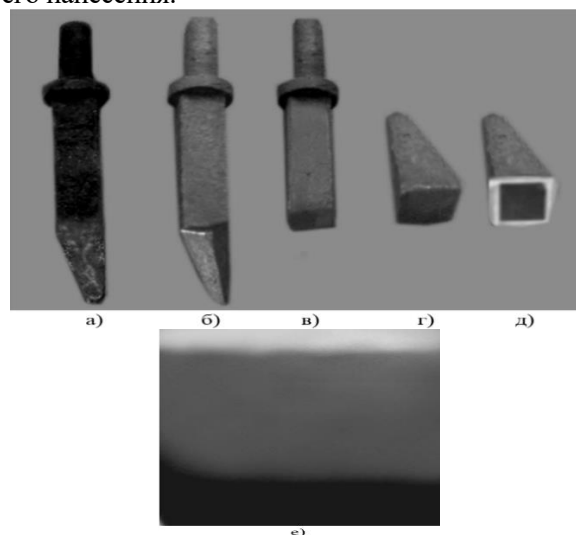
Готовые отливки деталей зубьев бороны и вырезанные образцы с твердосплавным сормайтовым покрытием с толщиной слоя от 2^х до 4^х мм: а-стальная деталь зубьев бороны; б,в-вырезанные куски образца детали; г-шлифованный и полированный образец; д-травленный образец с толщиной покрытия 2,5 мм; е-специально приготовленный стальной образец с толщиной слоя 3,0 мм.
